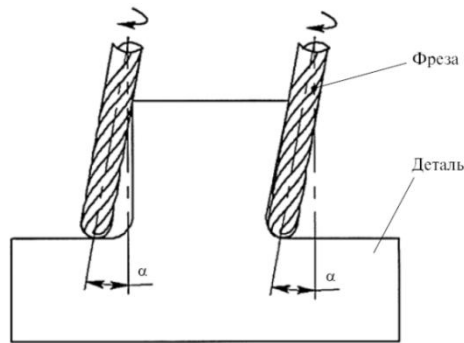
Схема отталкивания и затягивания фрезы малой жесткости при фрезеровании [98]
